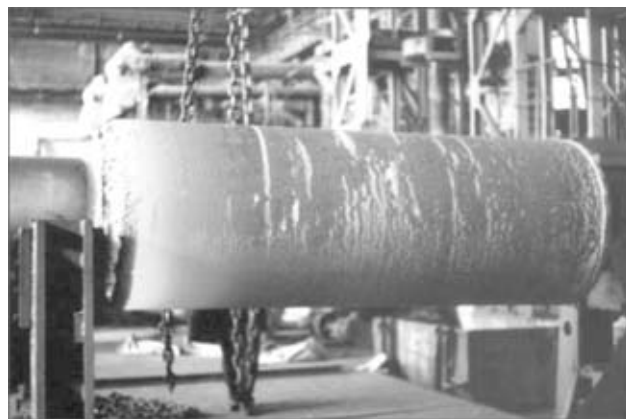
Внешний вид композитной заготовки ЭШН ЖПМ валка прокатного стана с рабочим слоем из быстрорежущей стали
